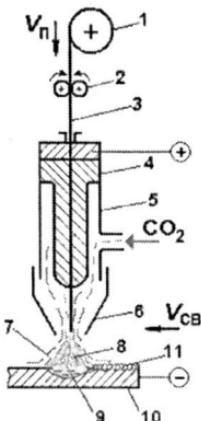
Схема сварки в углекислом газе
